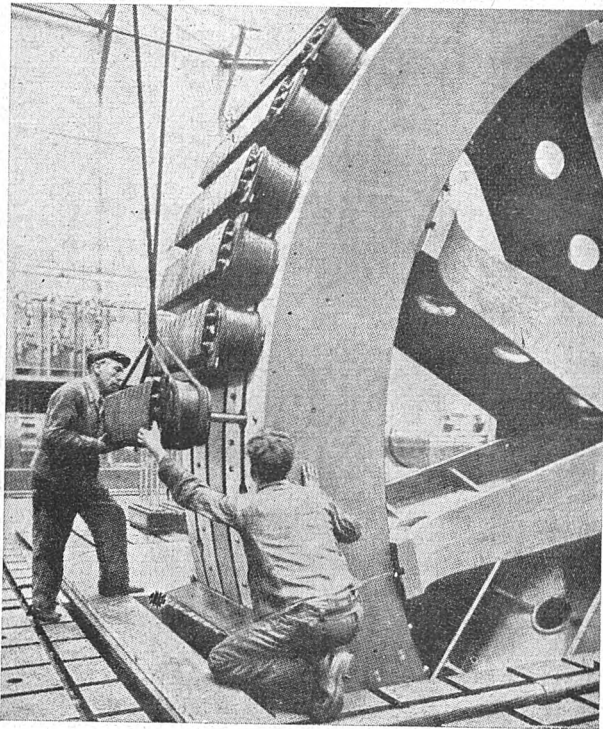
Wirnik pionowego generatora trójfazowego na 22 000 kVA, 100 obr./min. w czasie prób na zwykłą obro-
